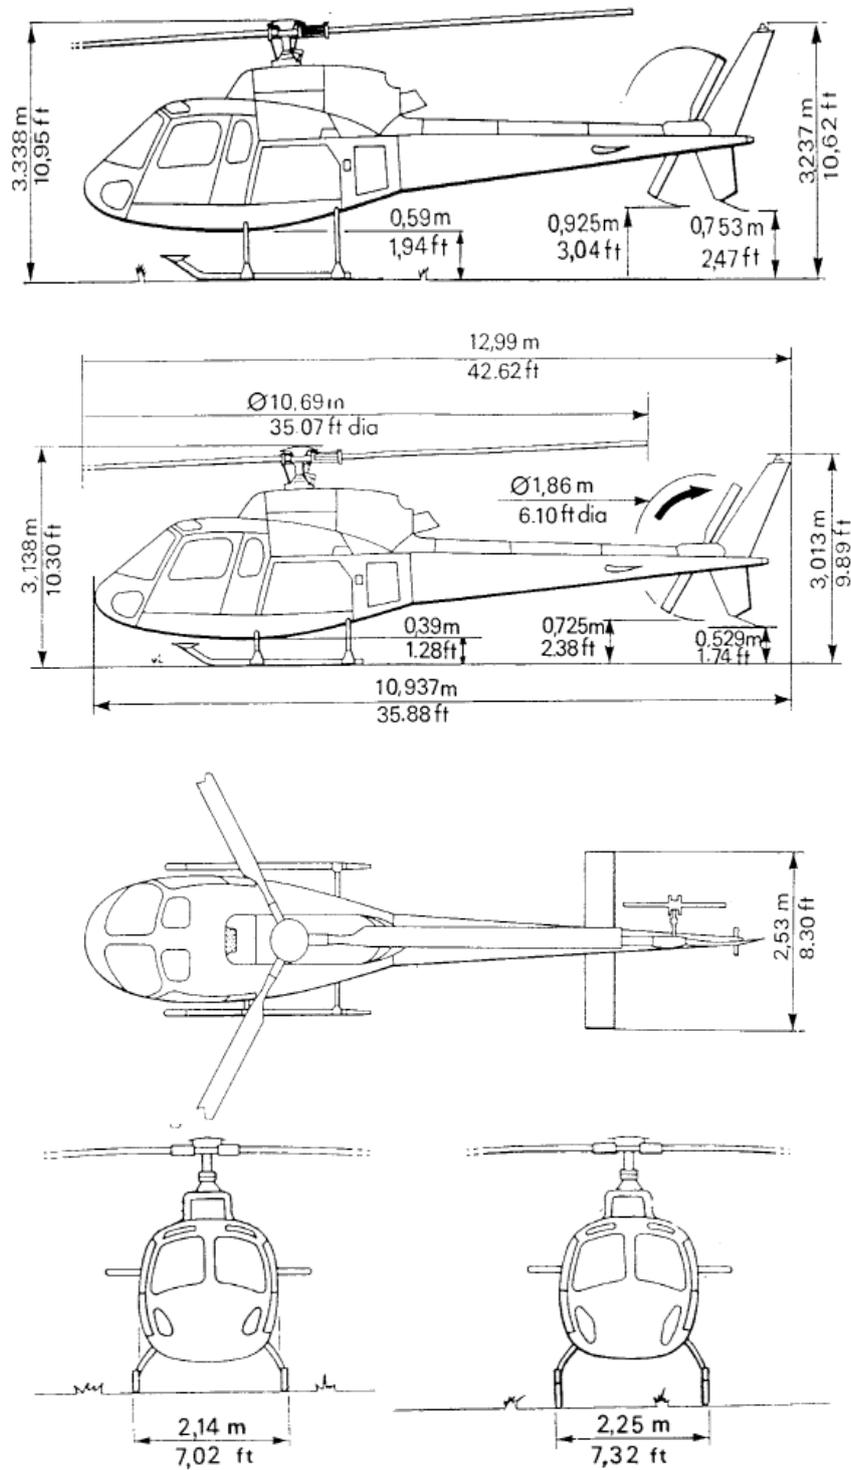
PRINCIPALES DIMENSIONES DEL HELICÓPTERO.
